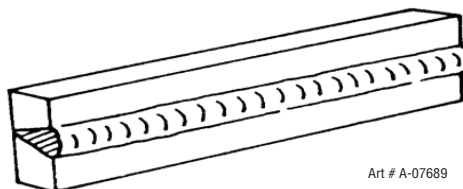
Position horizontale, soudure par aboutement
